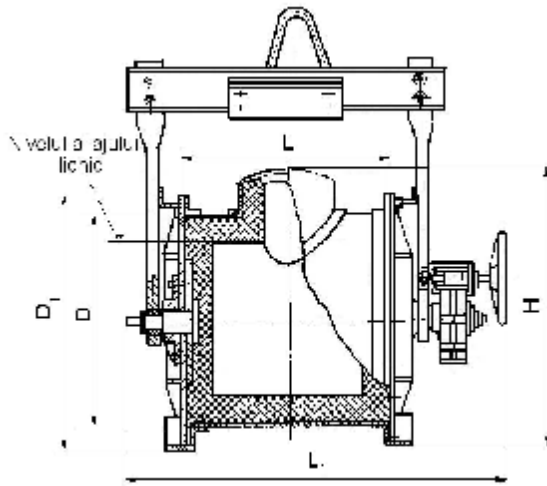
Oală transportată mecanic, tip tambur, cu turnare prin cioc
